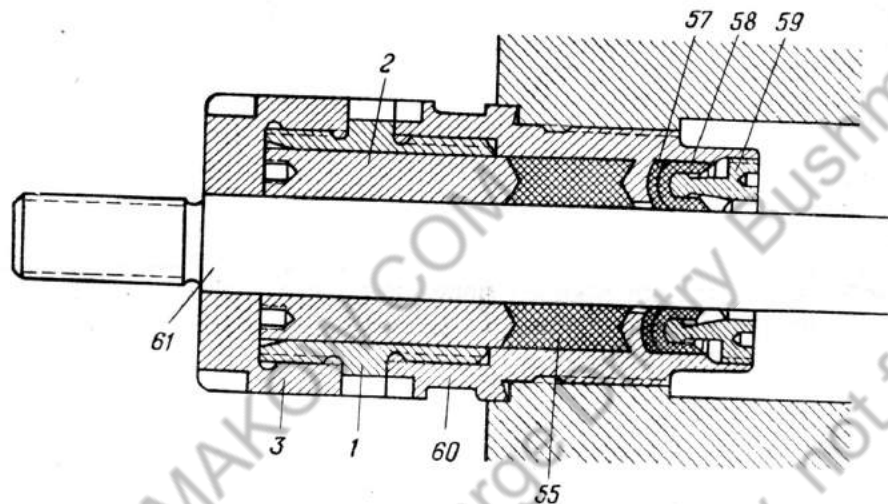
Поджатие сальника штока накатника при помощи прибора (сб. 42-20):
